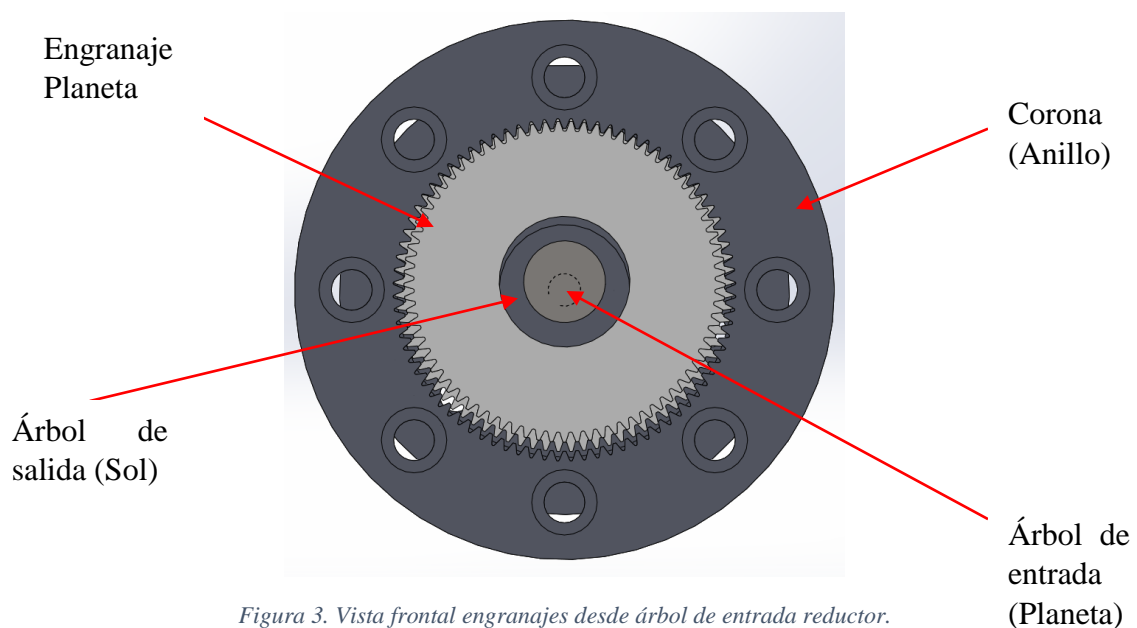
Vista frontal engranajes desde árbol de entrada reductor.
